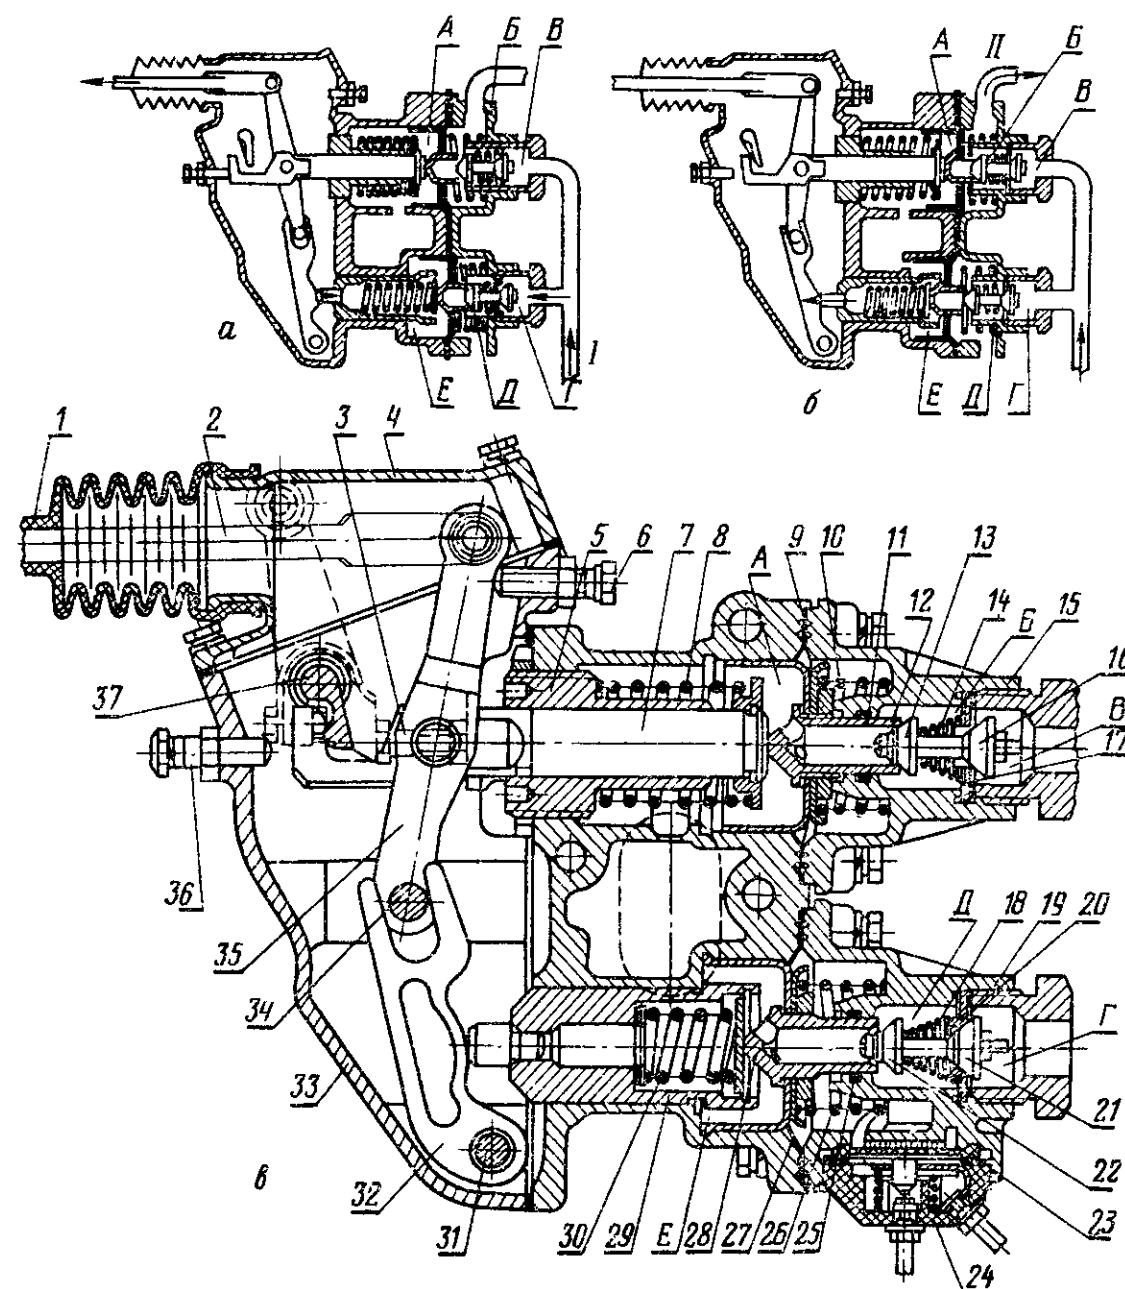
Тормозной комбинированный кран и схема его работы: а — при торможении; б — при отпущенных тормозах; 1 — чехол; 2 — тяга; 3 — винт регулировки свободного хода рычага ручного привода тормозов прицепа; 4, 15, 19 и 33 — крышки; 5 — направляющая штока; 6 — болт регулировки свободного хода рычага тормозного крана; 7 — шток; 8 и 30 — уравновешивающие пружины; 9, 23 и 27 — диафрагмы; 10, 14, 18 и 26 — пружины; 11 и 25 — уплотнительные кольца; 12, 17, 20 и 28 — седла клапанов; 13 и 22 — выпускные клапаны; 16 и 21 — впускные клапаны; 24 — датчик стоп-сигнала; 29 — стакан; 31 — ось; 32 и 35 — рычаги; 34 — палец; 36 — болт регулировки ограничения хода штока; 37 — кулачок; А, Б, В, Г, Д, Е — полости; I — из ресивера; II — в ресивер.
